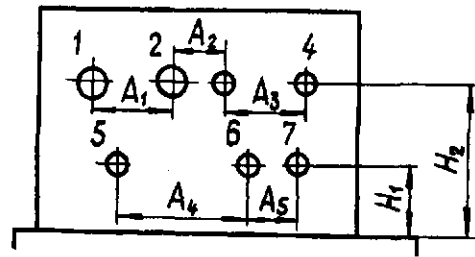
Схема расположения шпинделей (1...7) на агрегатно-расточном станке "с суммарными возможностями" для обработки группы деталей с унифицированными размерами по параметрам A и H
